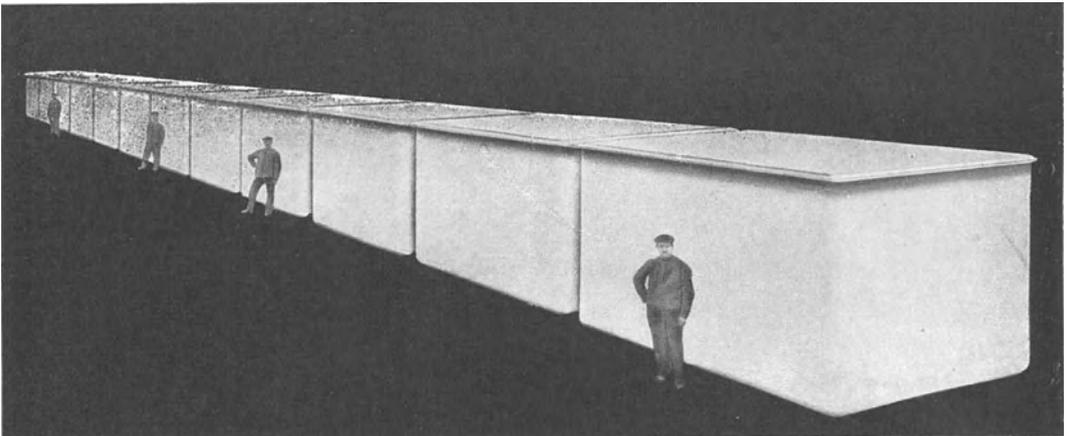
Nietlose, geschweißte Aluminiumbottiche für Brauereibetrieb.
